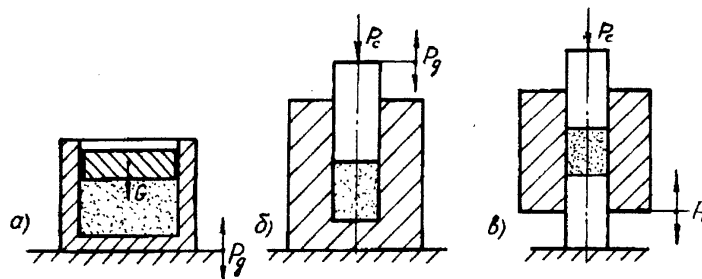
Схеми пресування заготовок у закритій прес формі при вібруванні контейнера (а), пуансона (б) та матриці (в)
